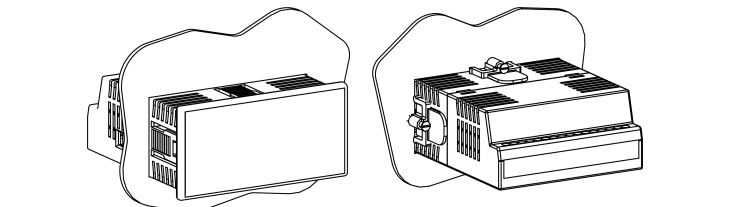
Монтаж прибора щитового крепления Щ2
